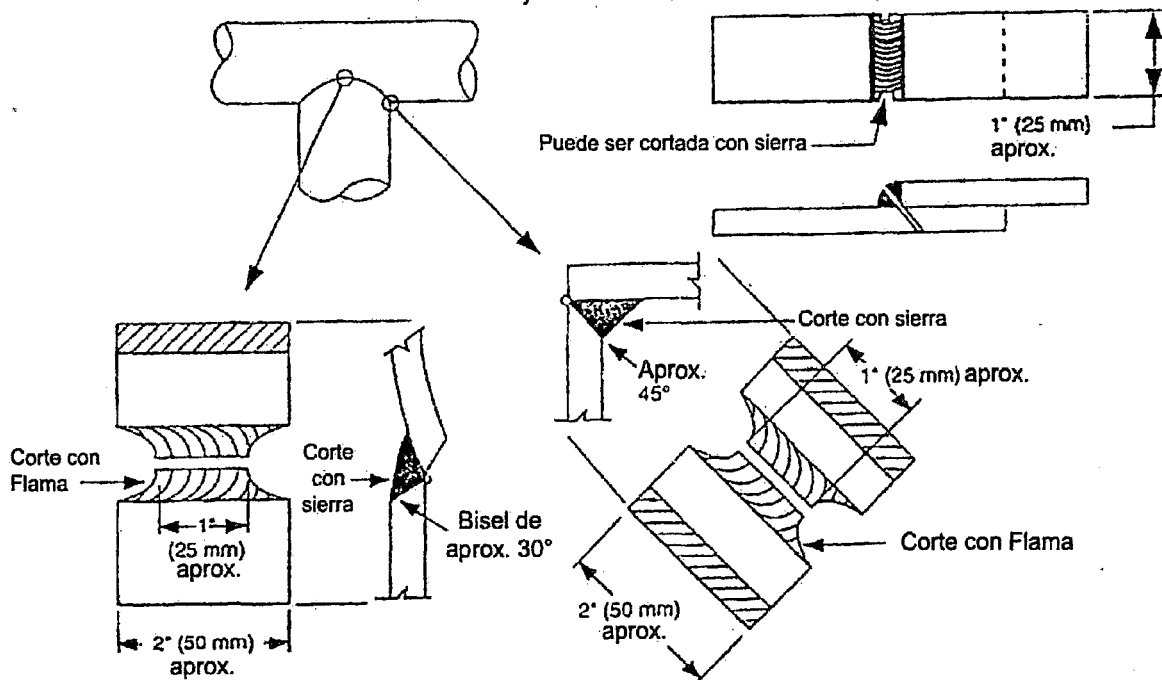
Ubicación de las Muestras para Ensayo de Rotura de Muesca: Soldaduras de Ensayo para Calificación de Procedimiento y Soldador con Soldadura de Filete, incluyendo, lado por lado, conexión con la rama.
